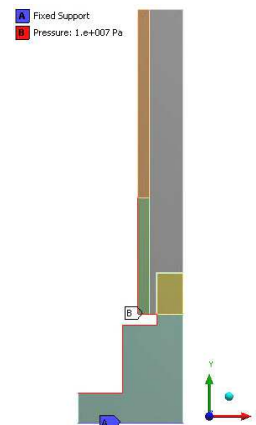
Переріз корпусу гідроциліндра із зовнішніми навантаженнями
